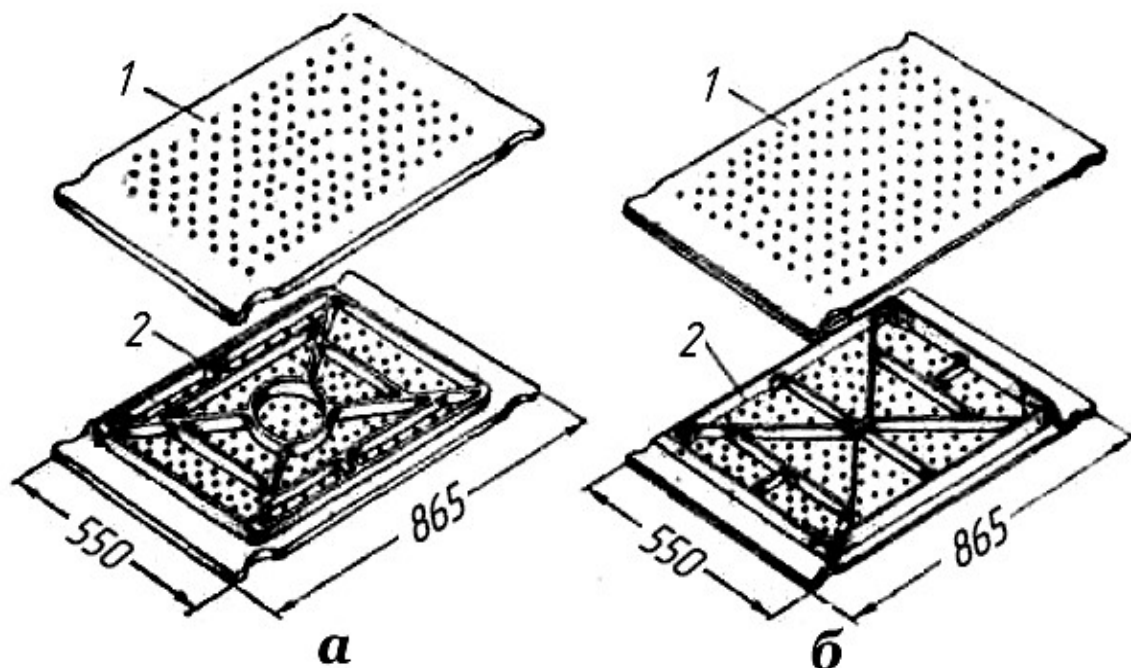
Плоские сушильные плиты: а – литая; б – сварная; 1 – вид сверху; 2 – вид снизу
